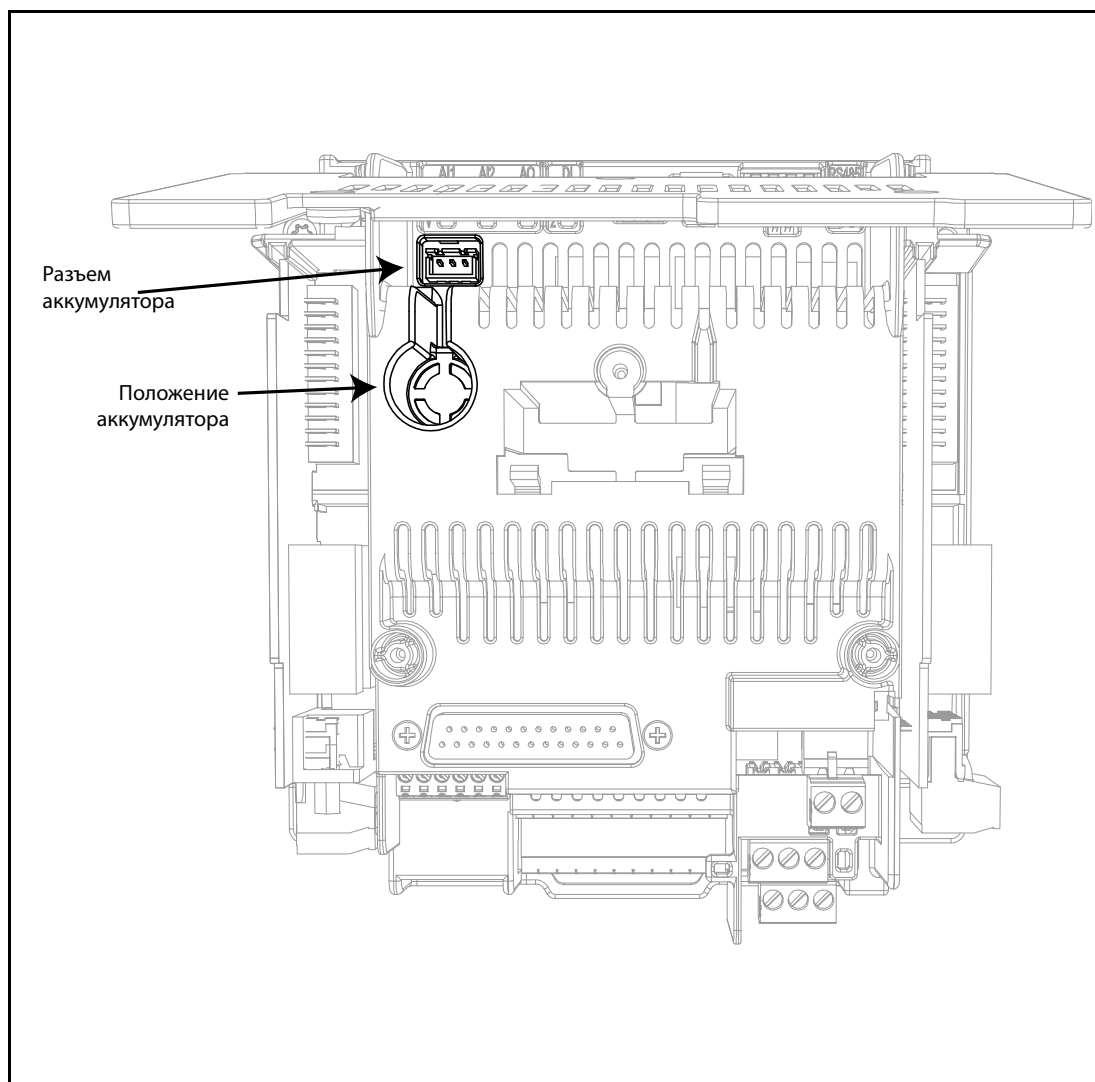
Положение и соединитель аккумулятора коробки управления.
